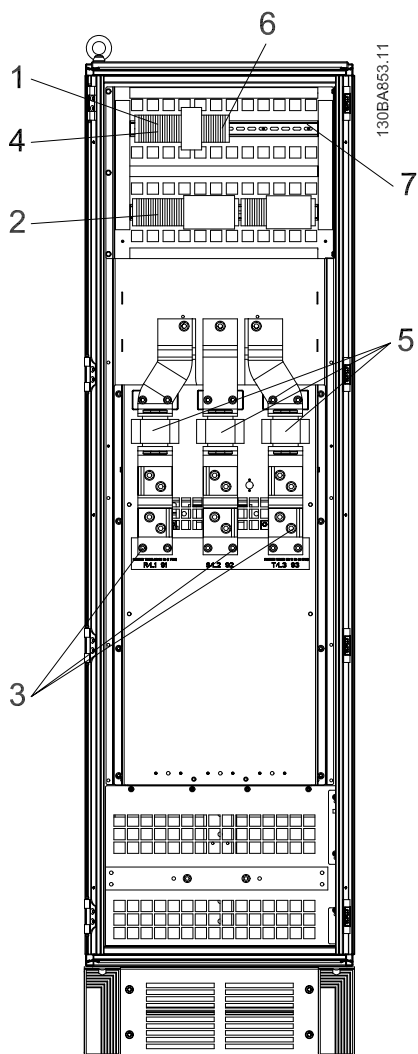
Шкаф для дополнительных устройств, корпуса F3 и F4
